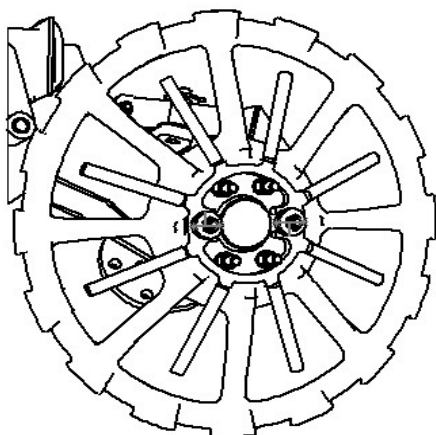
Колесо подъемника 53867 с наполнителем колеса горы центра
